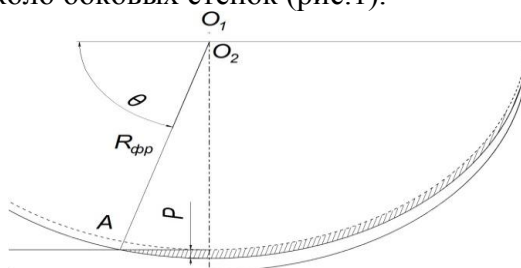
Схема фрезерования концевой радиусной фрезой вертикальной стенки близ дна.
